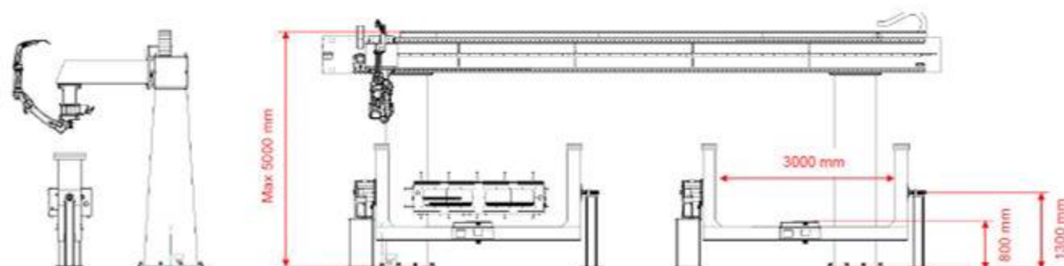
Příklad robotického svařovacího pracoviště od společnosti Valk Welding (Val-kwelding.com, 2021)
